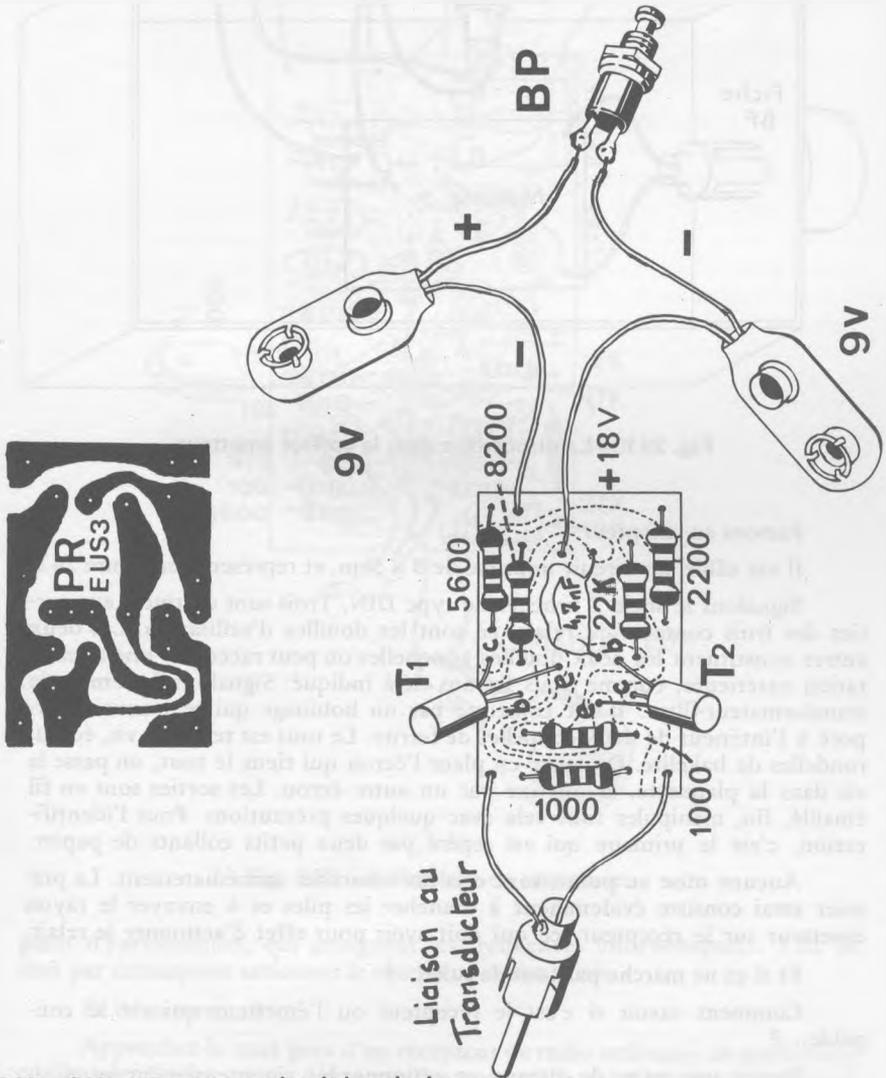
L'émetteur et son circuit imprimé, vu côté soudage.
